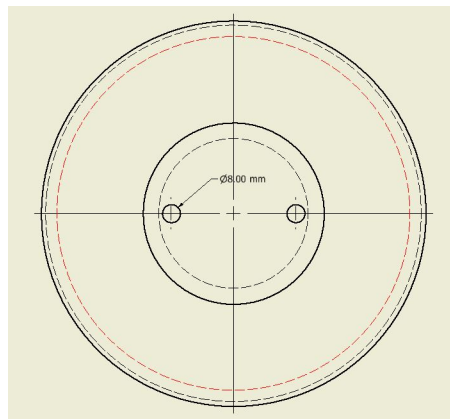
Quinto prototipo de la boya, parte de arriba (vista superior)
